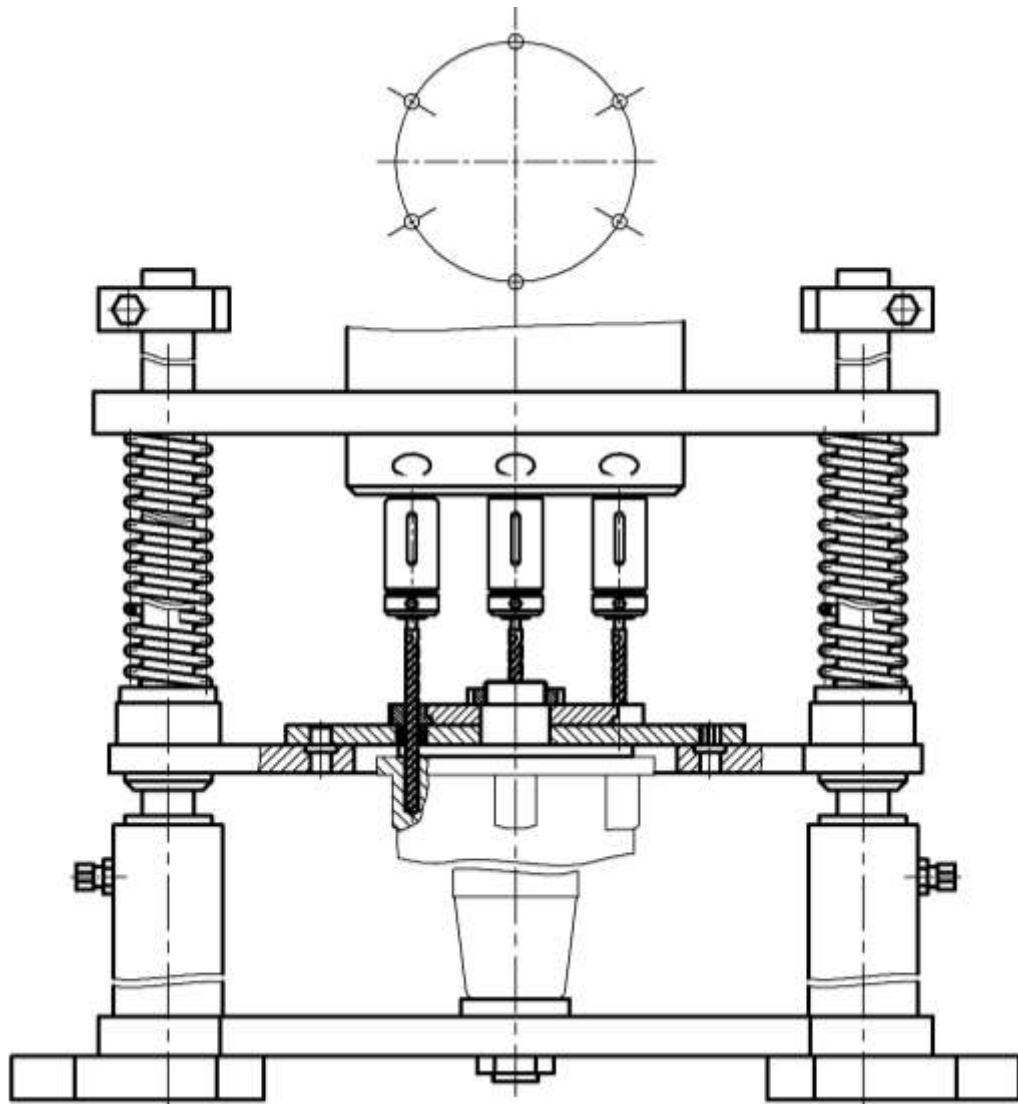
Загальний вигляд кондуктора для одночасного свердління
